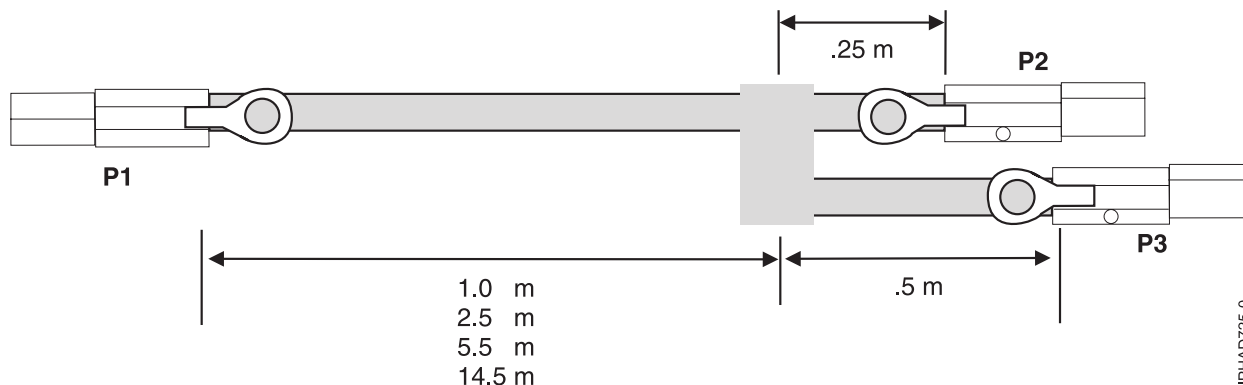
Comprimentos de cabo de montagem de cabo YO externo SAS
